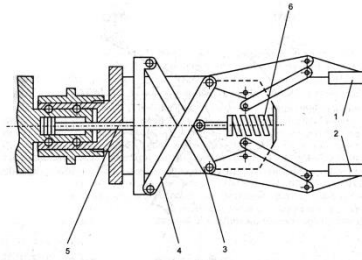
Двохпальцевий схоп: 1; 2 - пальці (губки); 3; 4 - важільна передача; 5 - шток пневматичного двигуна (пневмоциліндра); 6 - поворотна пружина
